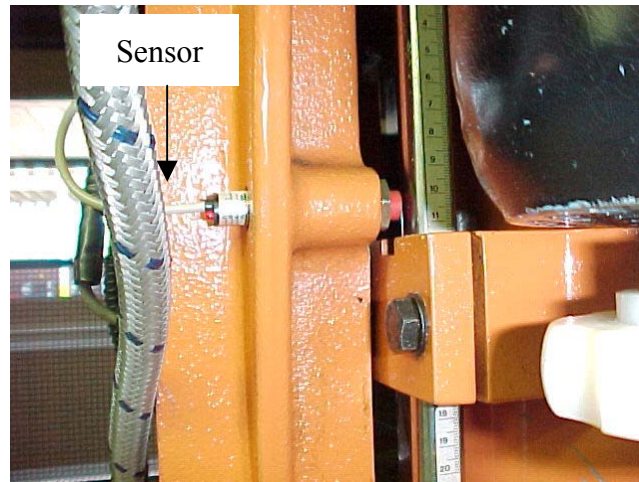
Sensor magnético implantado na máquina de corte automático
